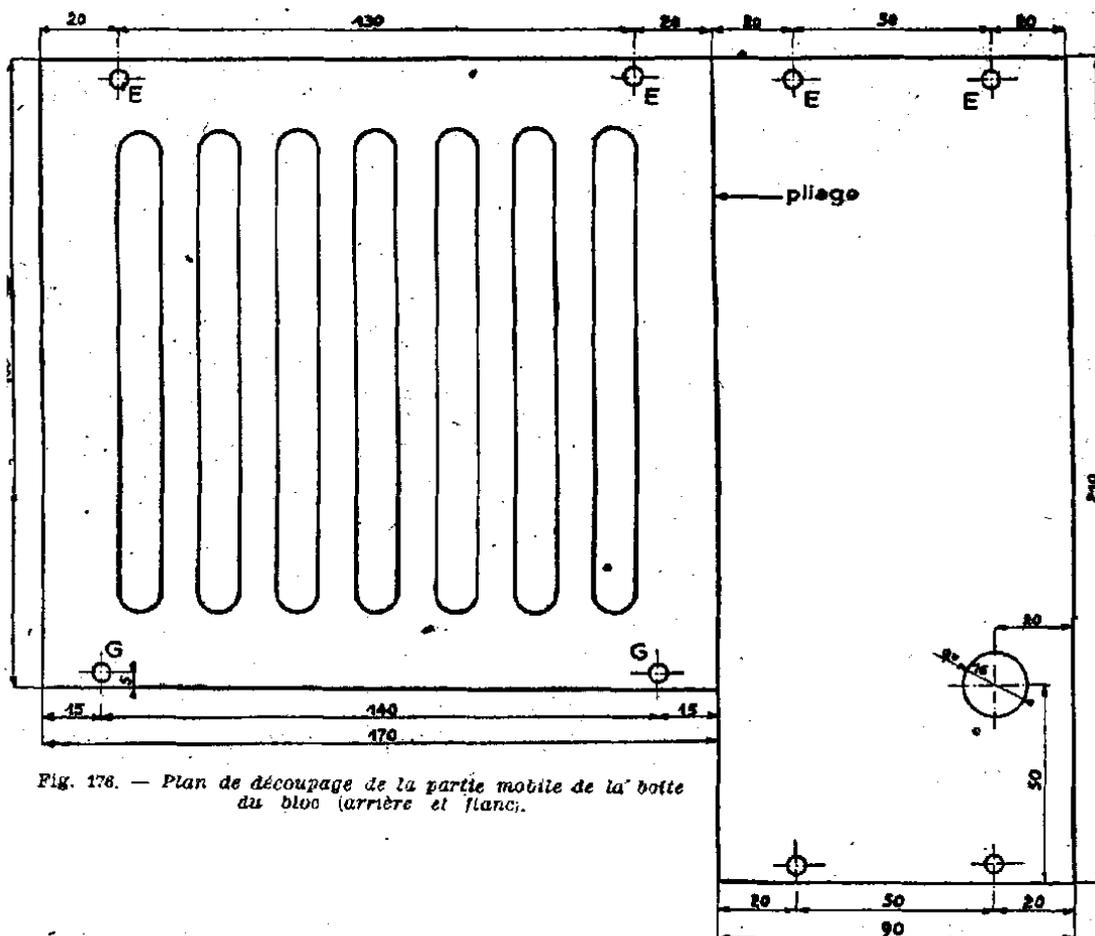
Plan de découpage de la partie mobile de la boîte au bloc (arrière et flanc).
